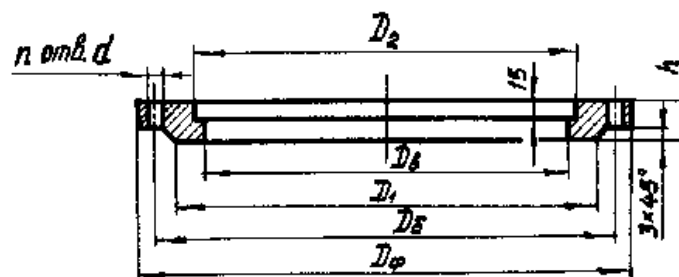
Конструкция фланца, выбранного для присоединения крышки к корпусу
